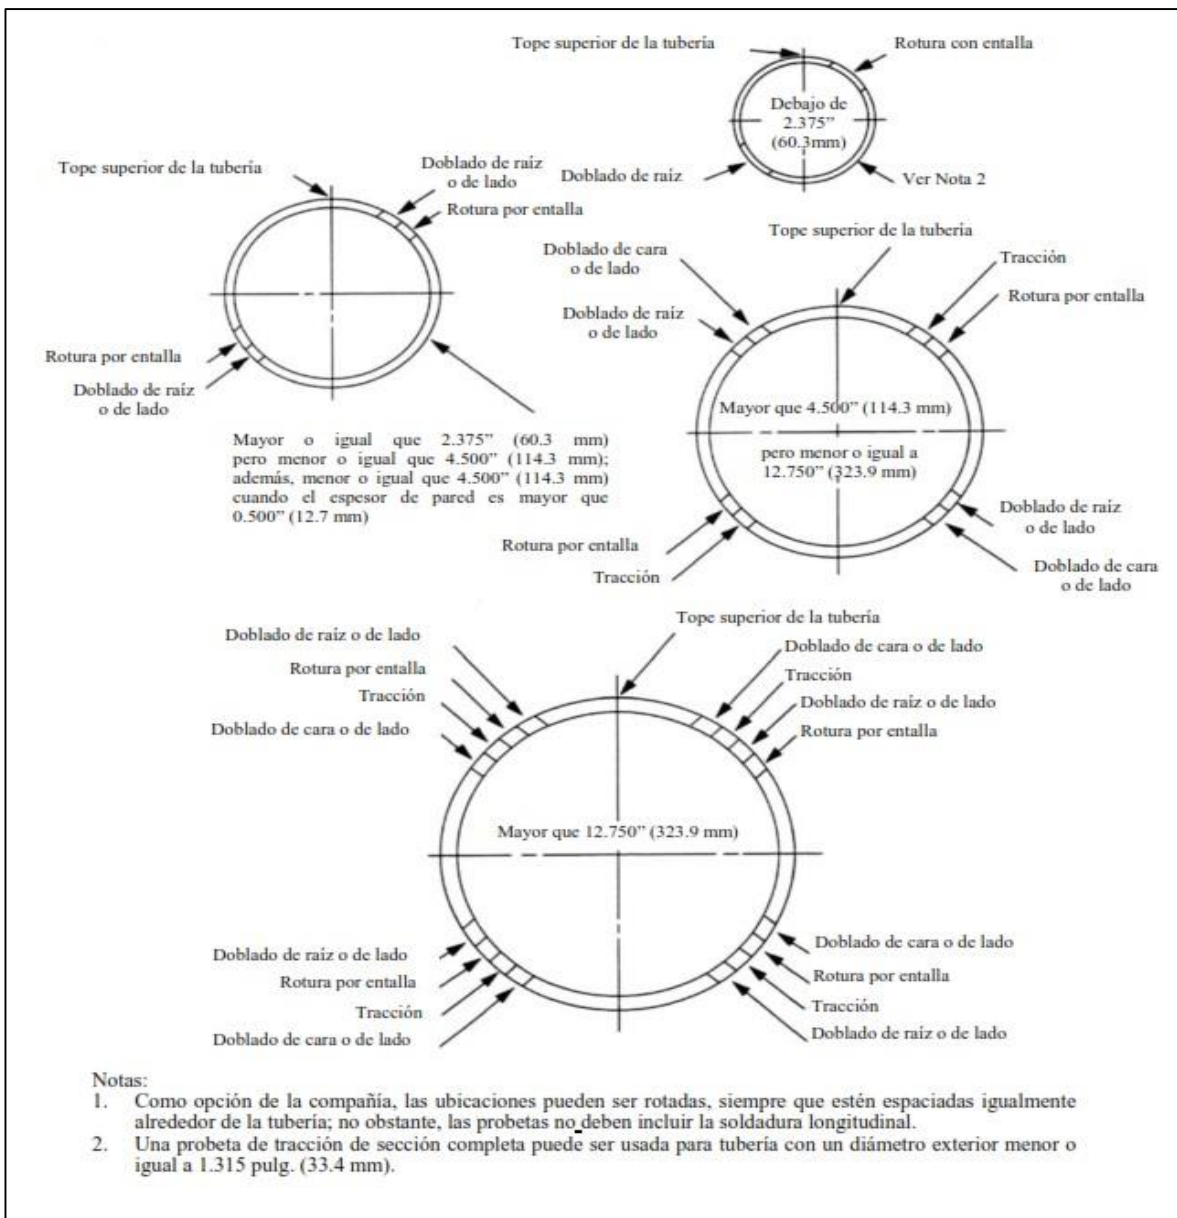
Ubicación de la probeta de ensayo de soldaduras a tope para ensayos de calificación del soldador
